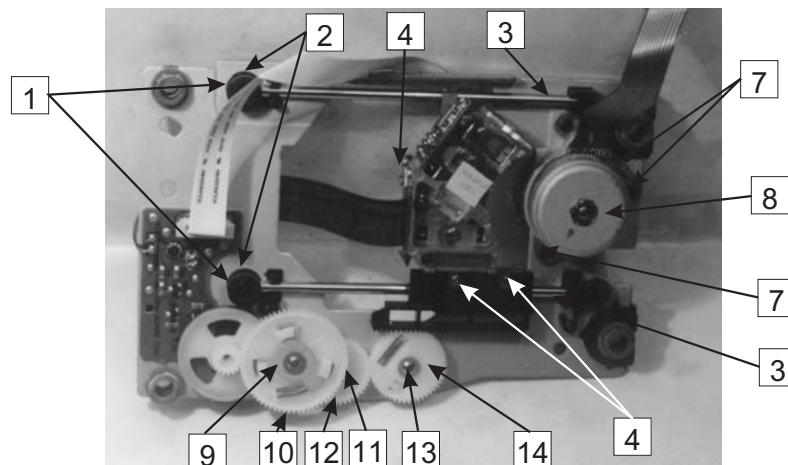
Внешний вид механизма привода дисков. Вид снизу
